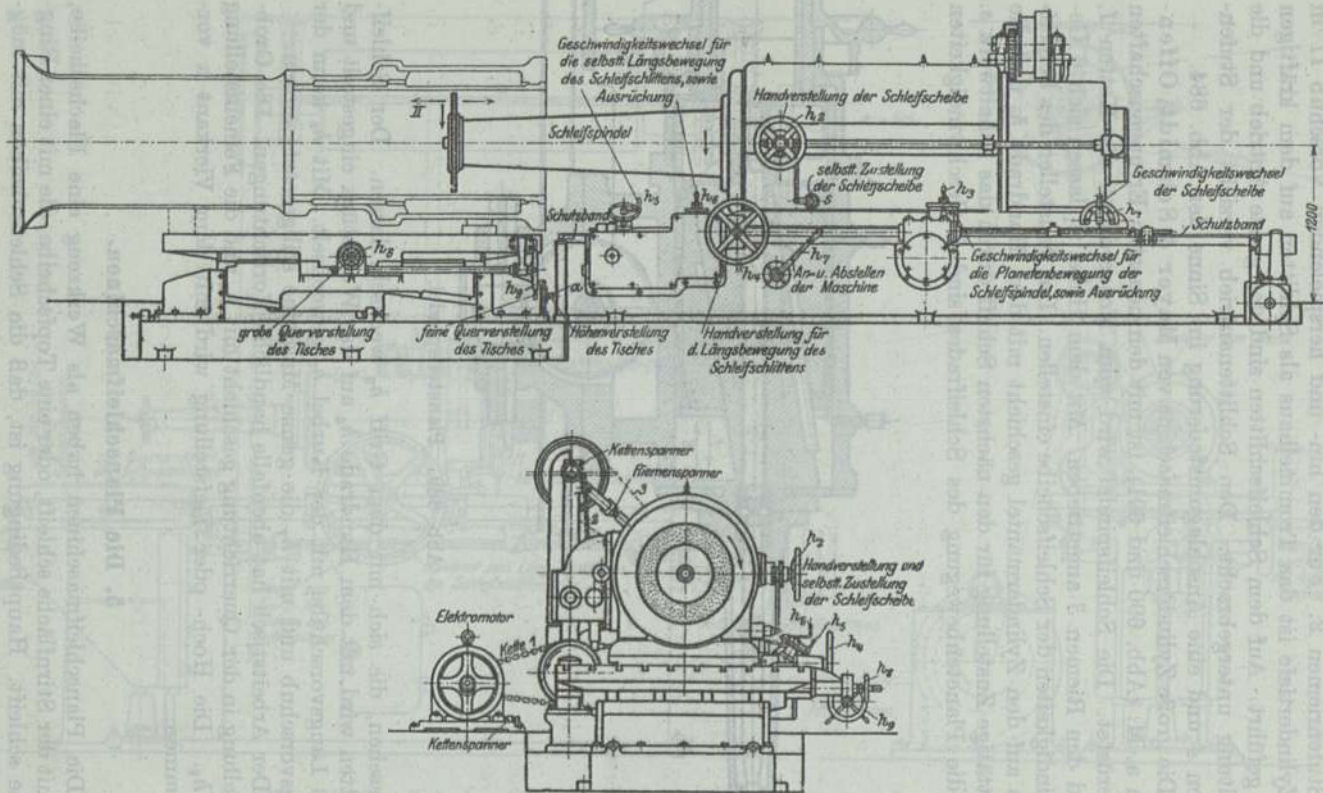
und 691. Große Zylinderschleifmaschine. Mayer &amp; Schmidt, Offenbach.
